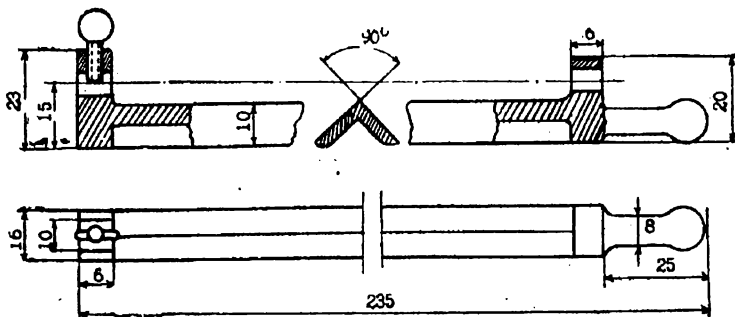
Приспособление для заточки пильных цепей ПЦУ-15 напильниками (державка напильника)
